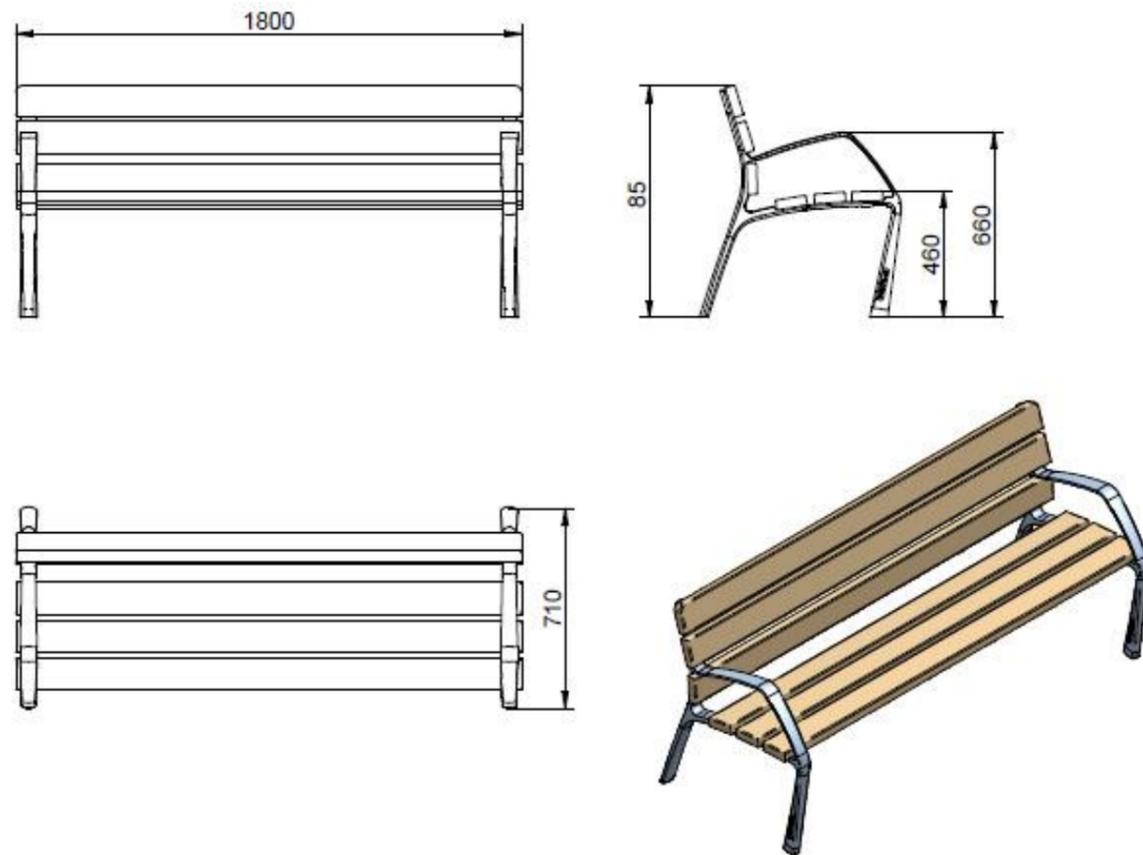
Vistas banco en la calle Muelle. Fuente: Benito.com.
